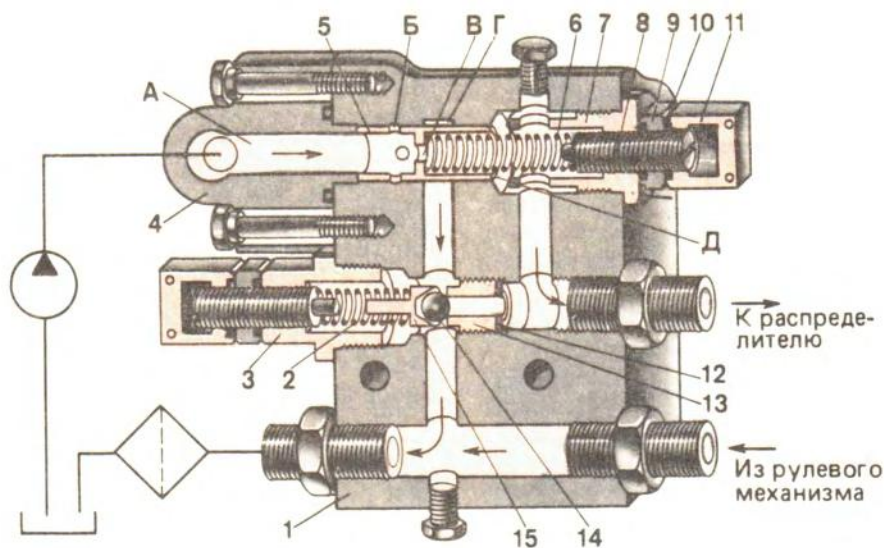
Клапан расхода масла гидроусилителем рулевого механизма трактора Т-150К:
